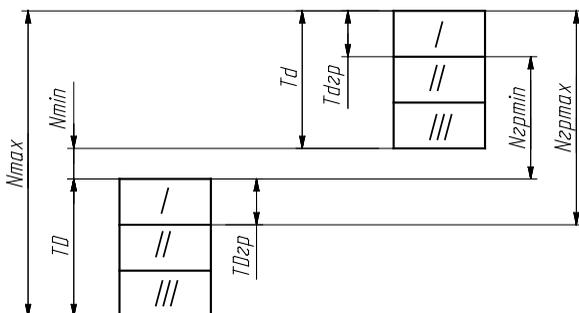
Схема полей допусков групп для селективной сборки
